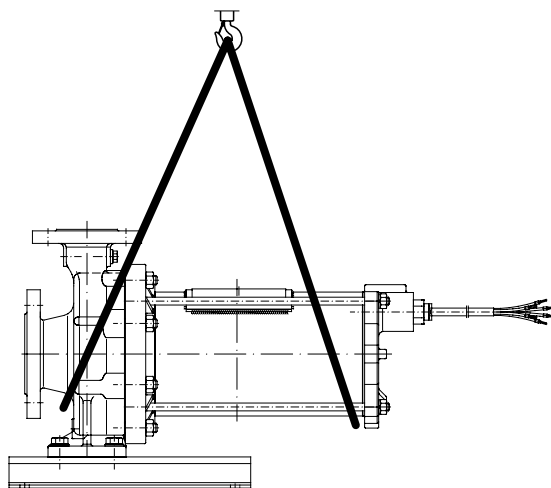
Hebezeug befestigen an Pumpenaggregat mit Grundplatte
